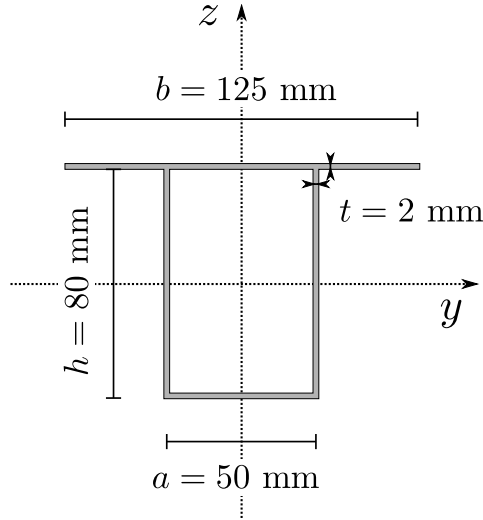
Géométrie de la section de la poutre caisson
